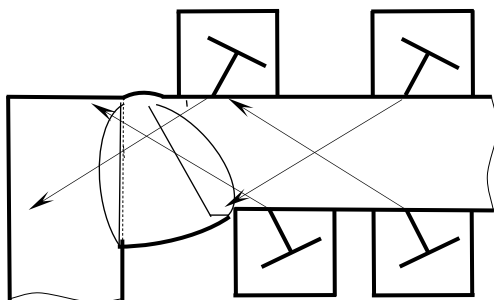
Схема контроля угловых сварных соединений прямым лучом
